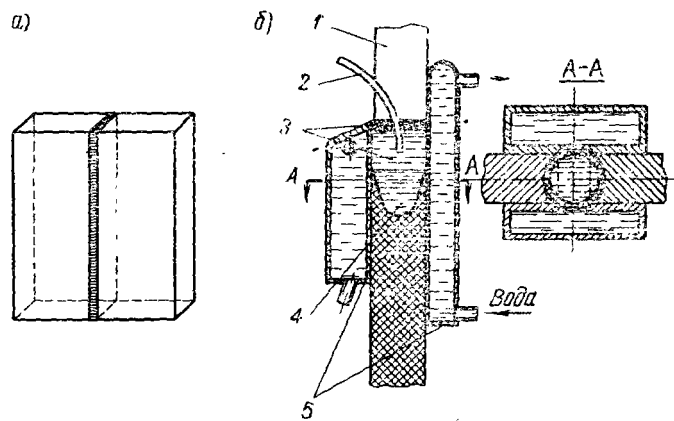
Соединения при электрошлаковой сварке:
